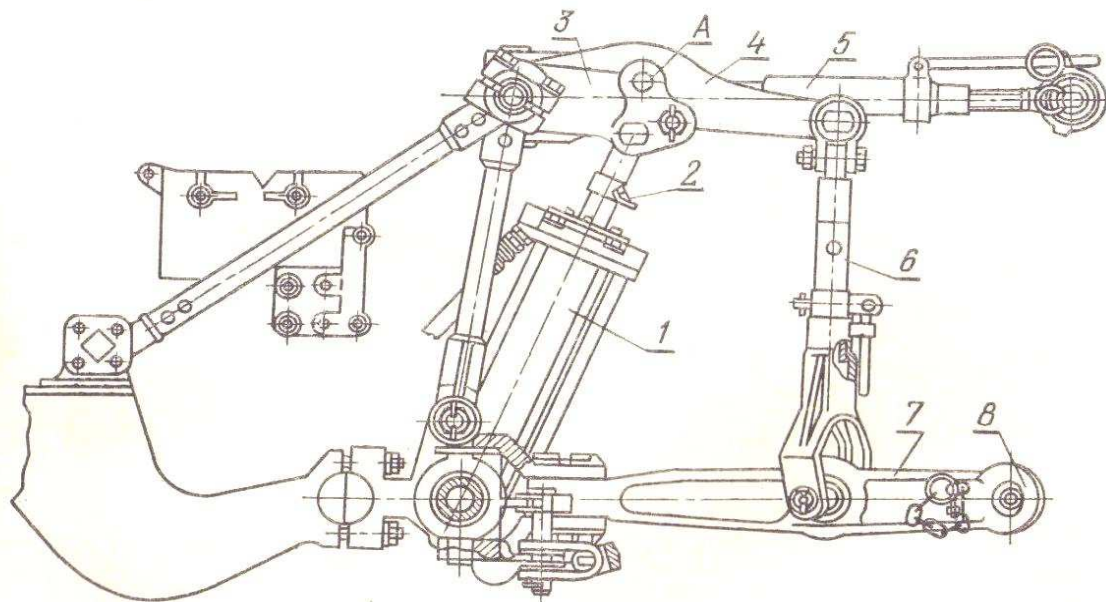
Механизм навески трактора: 1 – гидроцилиндр; 2 – передвижной упор; 3, 4 – рычаги; 5 – верхняя тяга; 6 – раскос; 7 – нижняя тяга; 8 – шаровая втулки
